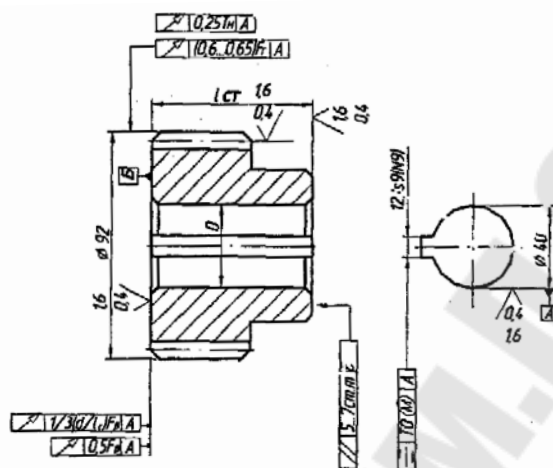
Зубчатое колесо с типовыми требованиями к точности его изготовления
